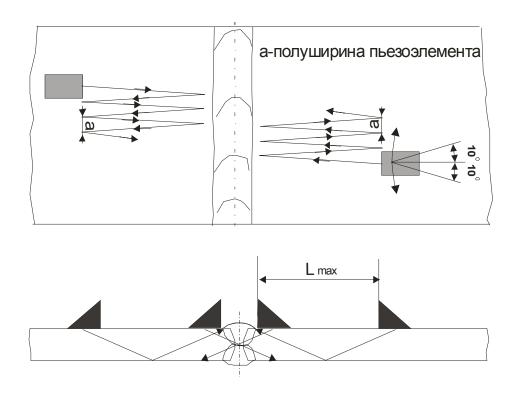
Схема контроля стыкового сварного соединения
